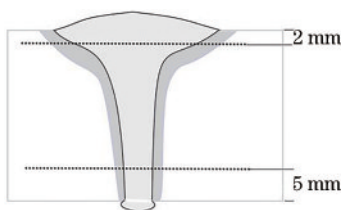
焊缝横截面显微硬度测试位置示意图
